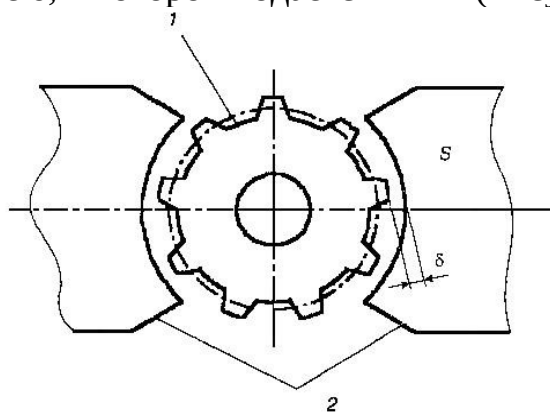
Схема магнитно-абразивной обработки зубчатых колес.
